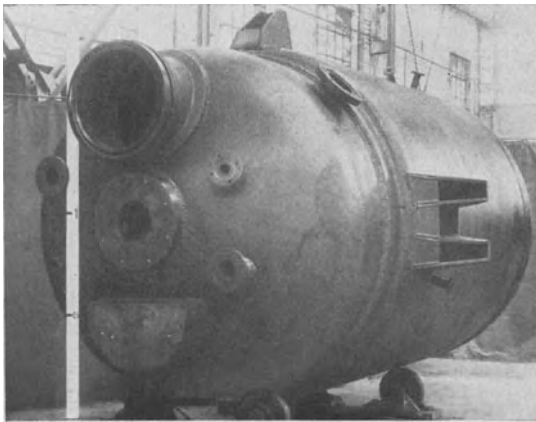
Geschweißter doppelwandiger Kessel.
